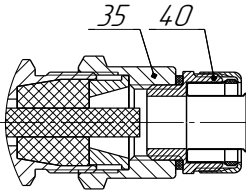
(лист 2 из 4) – Чертеж средств взрывозащиты варианта со сварным корпусом из нержавеющей стали (НЖ)
